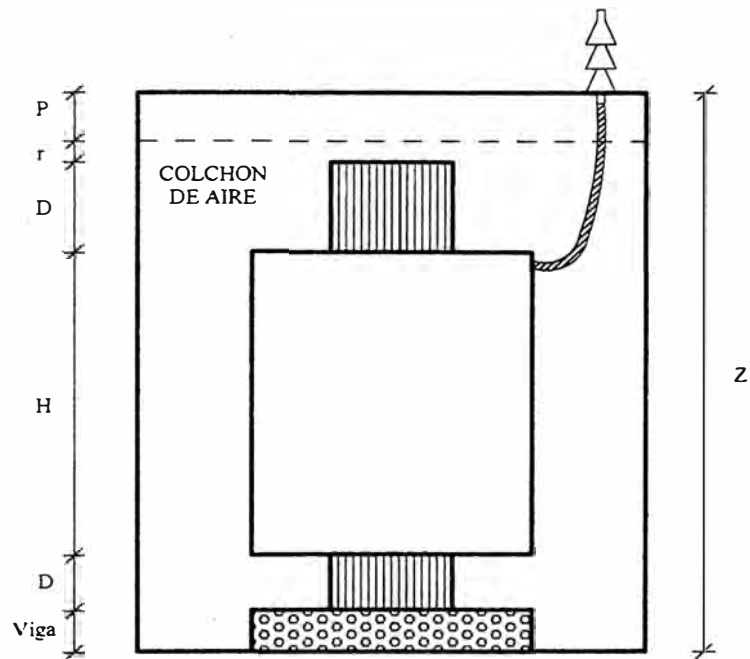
Vista de corte y las dimensiones del transformador de puesta a tierra.
